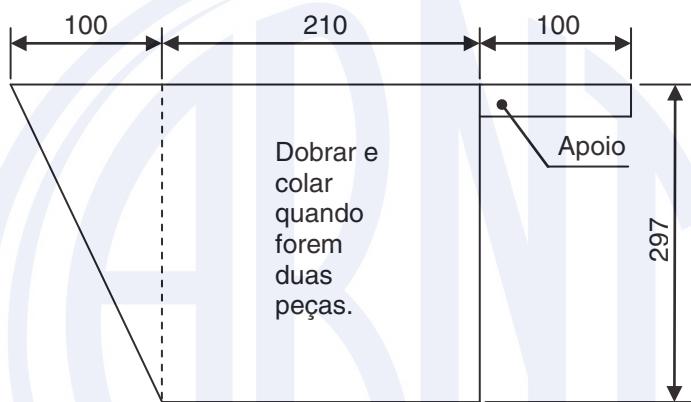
(b) – Molde para dispositivo – Dimensões em mm
